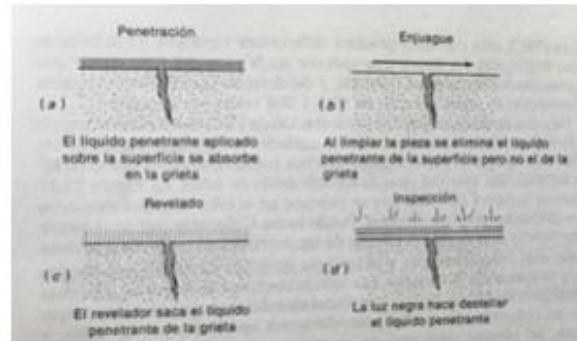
Aplicación de líquidos penetrantes en las soldaduras
